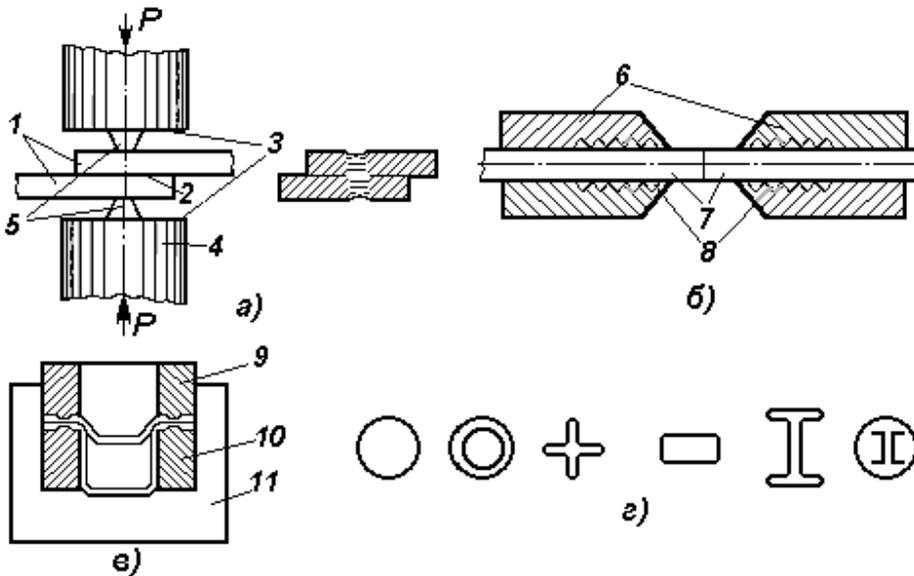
Принципиальная схема холодной сварки
